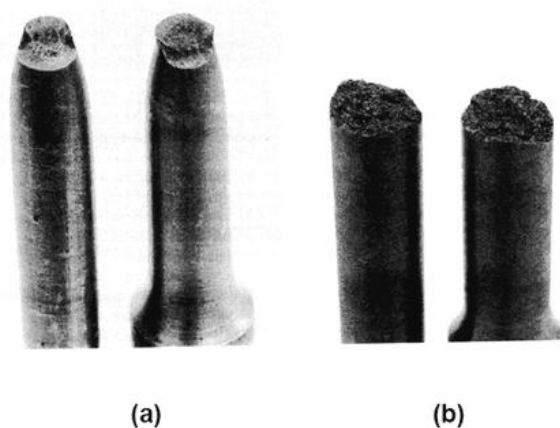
(a) Fractura dúctil (b) Fractura frágil (Fonte: www.monografias.com)
